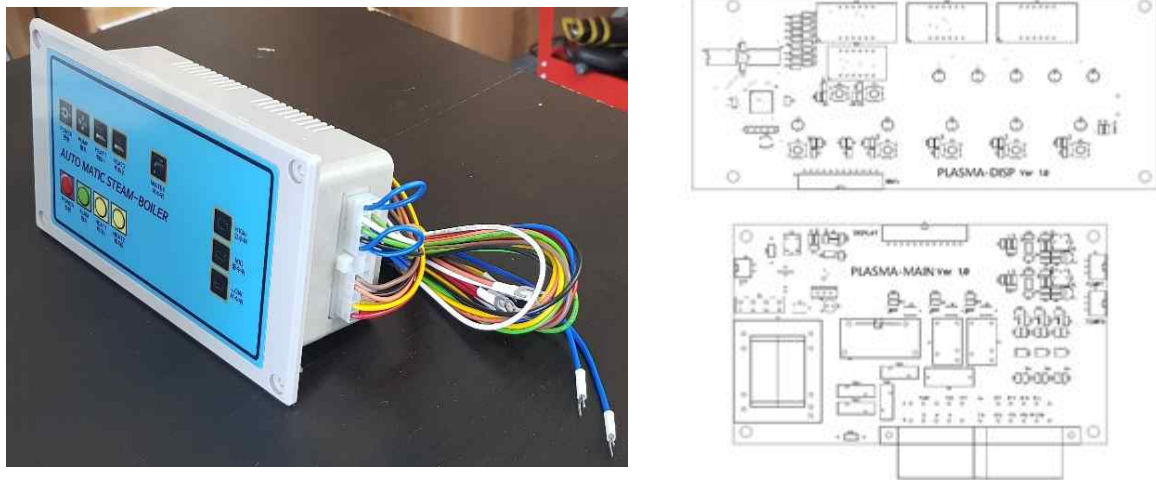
플라즈마 보일러 전용 micom controller 및 PCB 실장도
